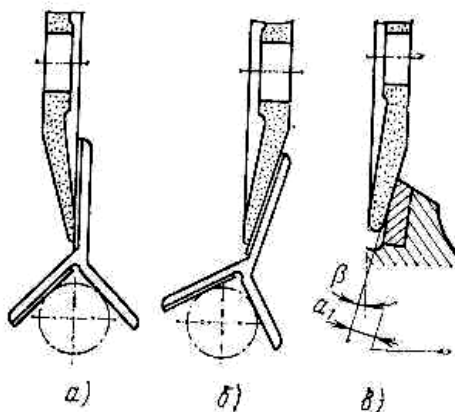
Схема установки шлифовального круга при заточке передней поверхности инструмента:
